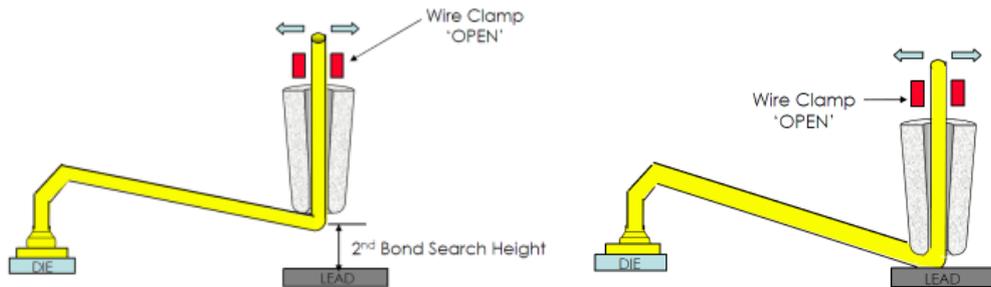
Схема формирования 2-го сварного соединения «клин»
